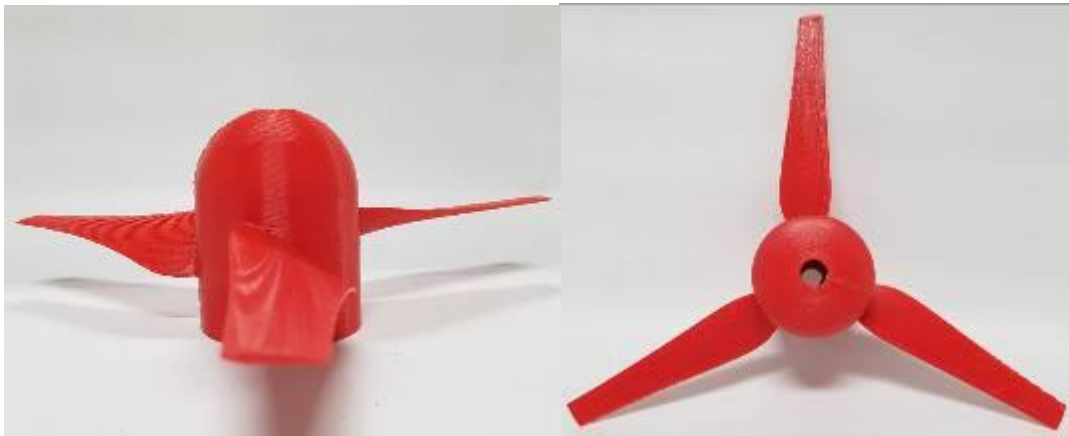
Rotor NREL S802 con manufactura aditiva. Fuente: autor.
